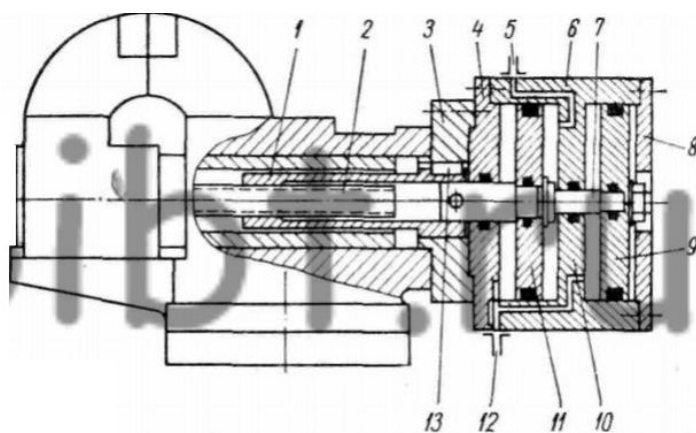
Схема конструкции тисов с пневматическим приводом.
